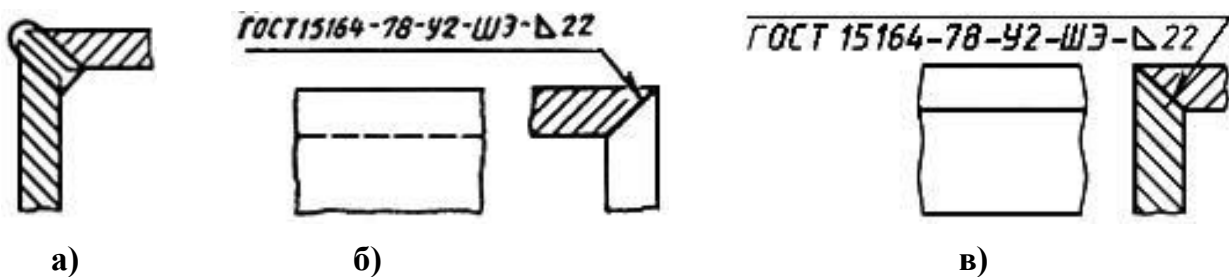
Пример обозначения сварного шва [5]: а – форма поперечного сечения шва; б – обозначение с лицевой стороны; в – обозначение с оборотной стороны
